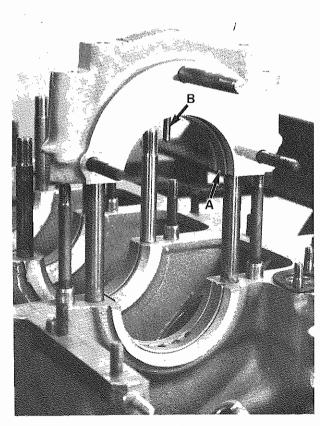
A) Cuscinetto - B) Frangiolio A) Bearing - B) Oil breaker
